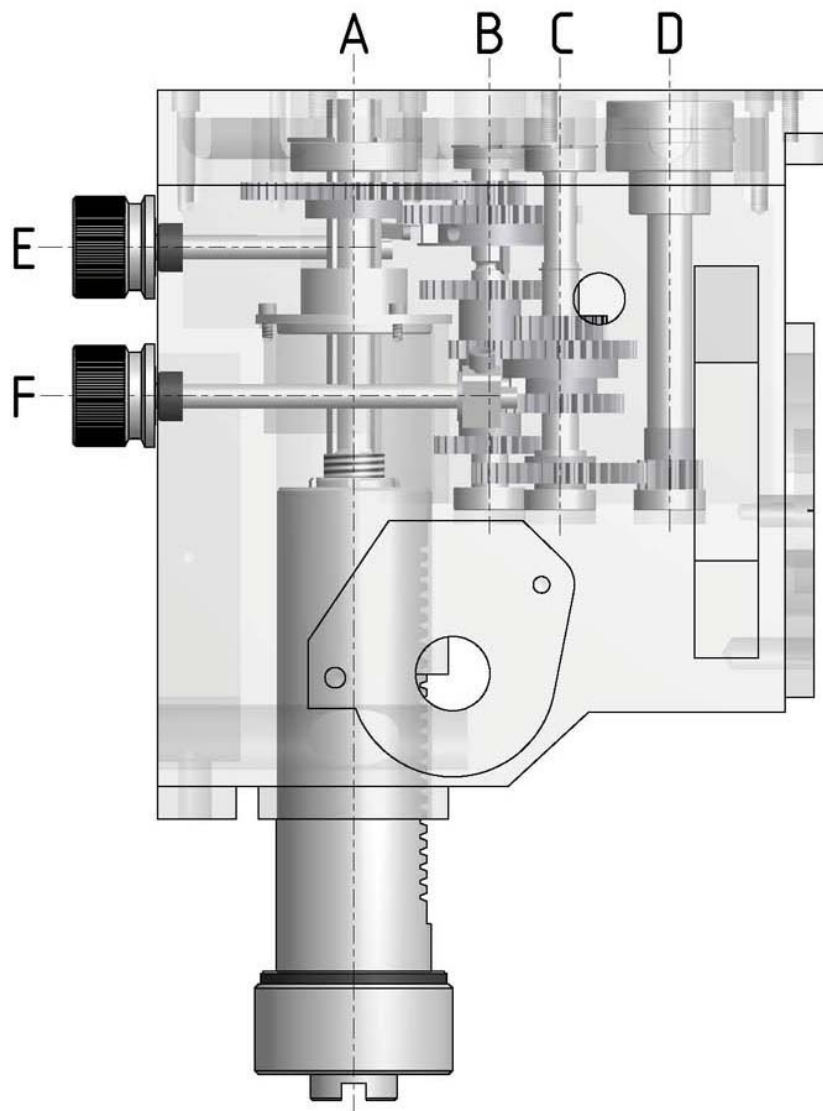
Fräskopf 1 von 6 - Cabezal fresador 1 de 6
